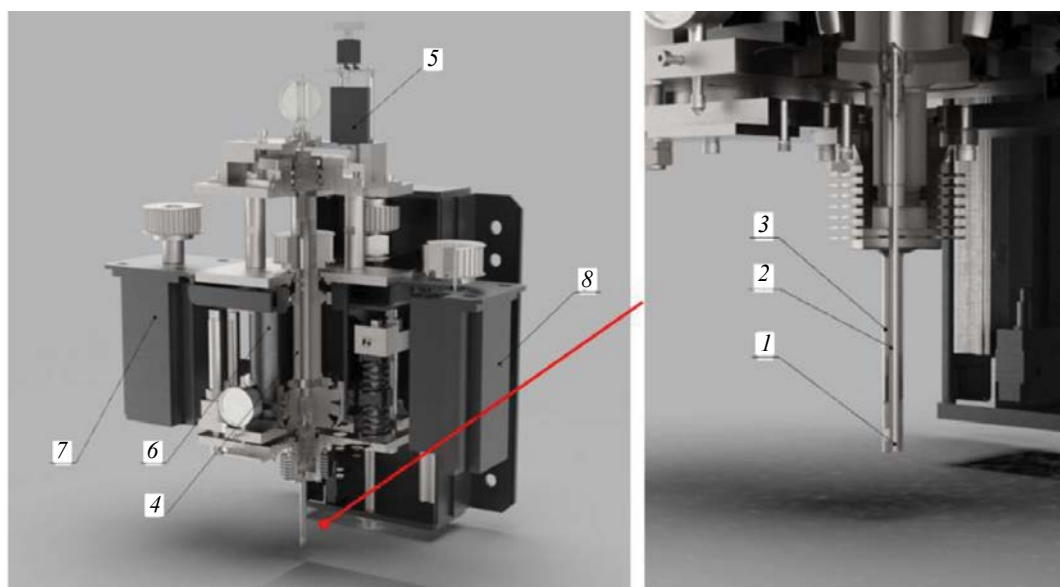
Трехмерная модель сварочной головы ТСТП:
